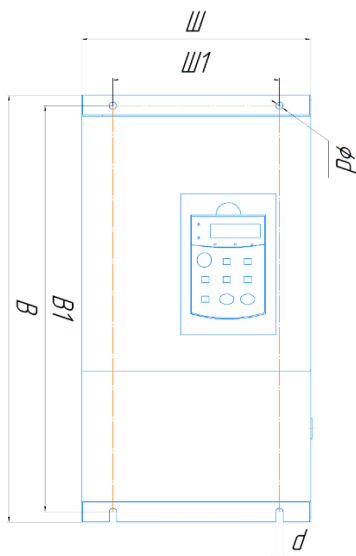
б – габаритные и установочные размеры LCI в металлическом корпусе
